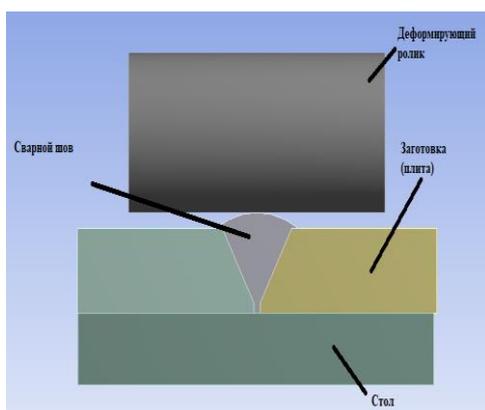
Упругая твердотельная модель ролика и сварного соединения
